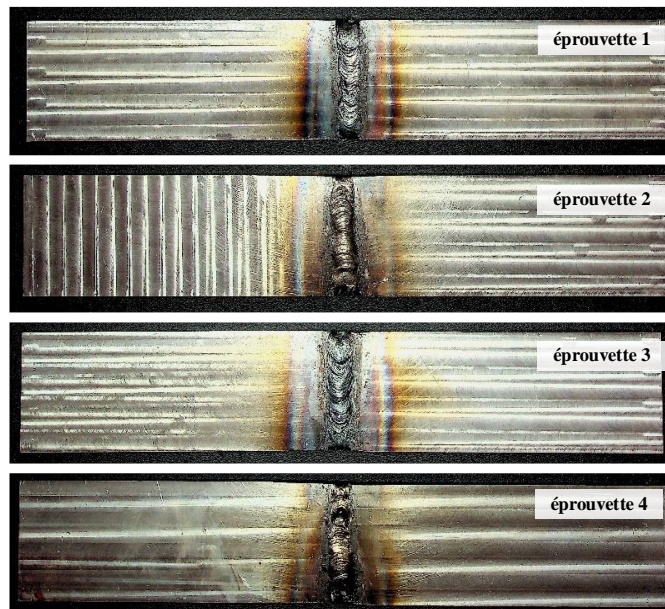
Eprouvettes soudées bout à bout
